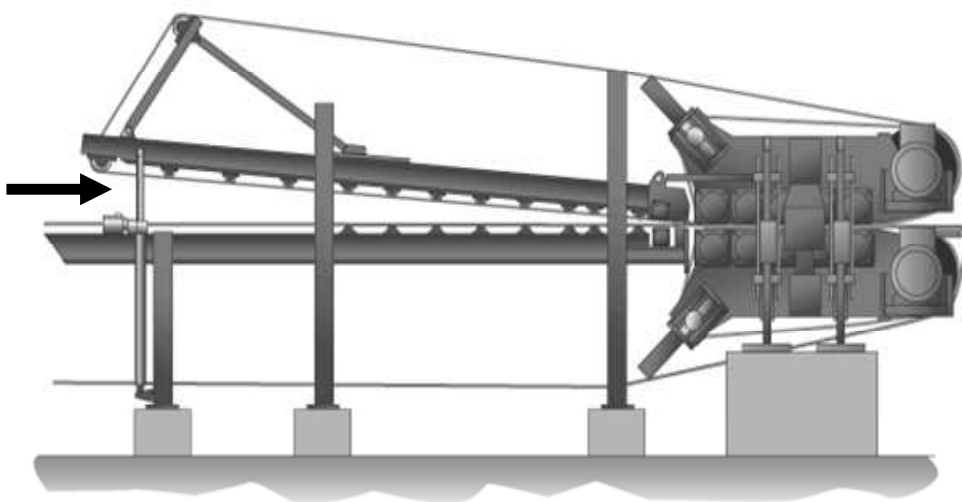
Проходной ленточно-валковый пресс для подпрессовки стружечного или волокнистого ковра
